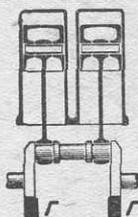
Схема двухцилиндрового двигателя с кривошипами, направленными в одну сторону.
